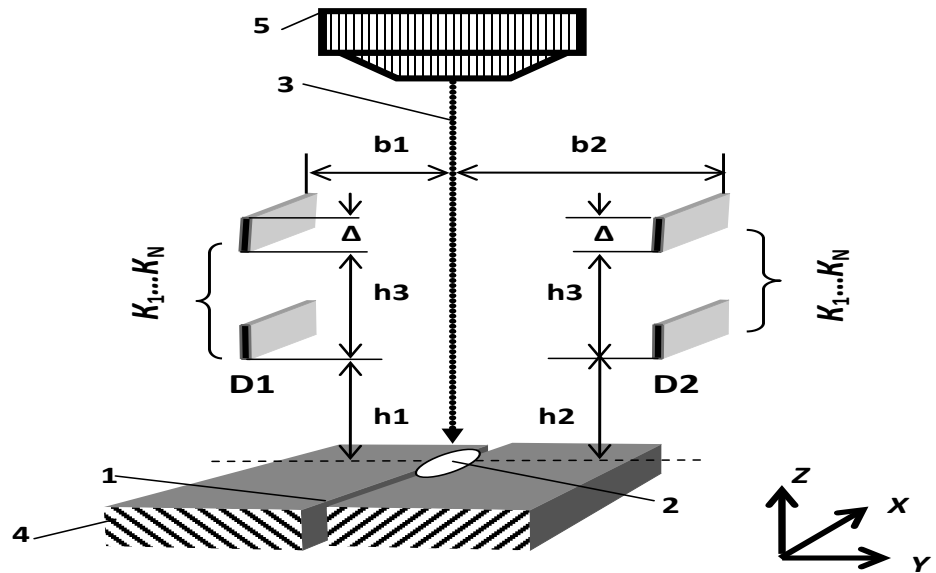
Пространственное расположение одиночных коллекторов относительно сварочной ванны и оси сварочного пучка: 1 - стык; 2 - сварочная ванна; 3 - ось сварочного пучка; 4 - изделие; 5 - электронно-лучевая сварочная пушка; b_1, b_2 - расстояние датчик - ось пучка, мм; h_1, h_2 - расстояние датчик - поверхность, мм; h_3 - расстояние между коллекторами; $K_1 \dots K_N$ - одиночные коллекторы; $D1$ и $D2$ - датчики положения стыка; Δ - ширина коллектора, мм
